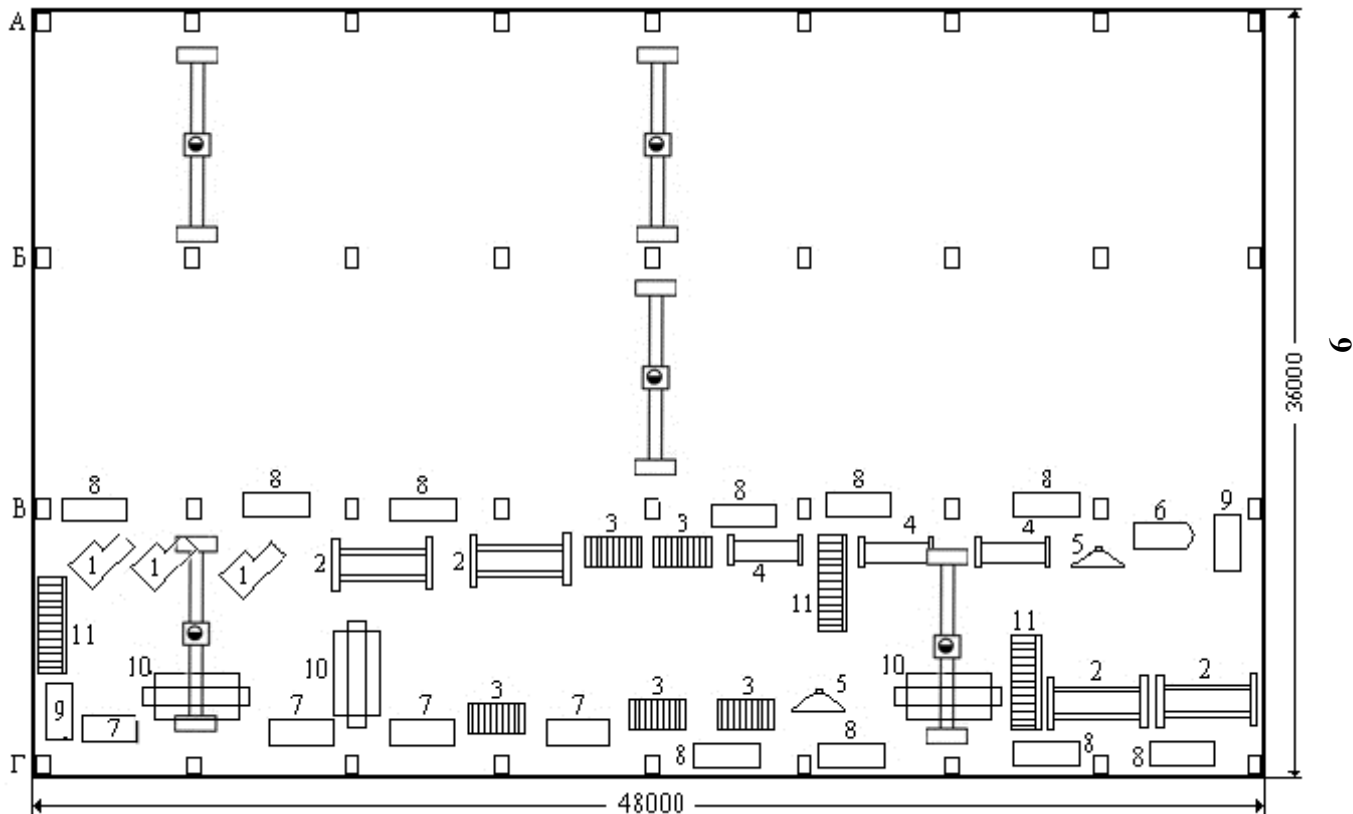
Схематичний план заготівельно – зварювального цеху.
